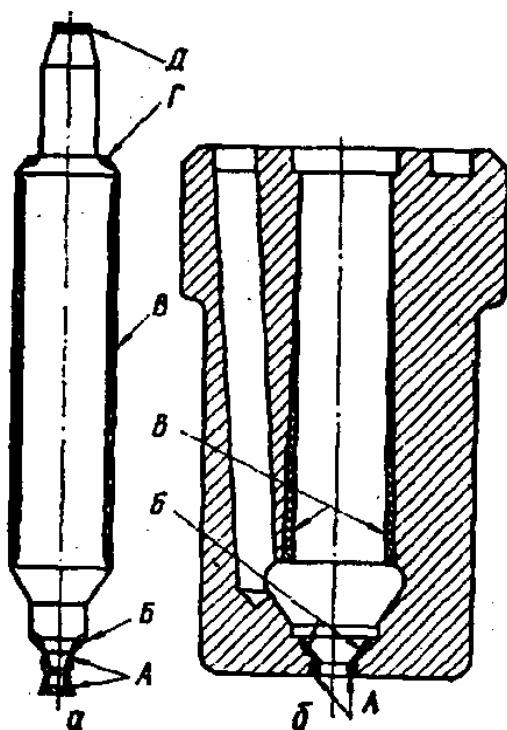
Місця і характер спрацювання деталей розпилювача штифтової форсунки: а – поверхонь голки; А – штифта; Б – запірного конуса; В – напрямної частини; Г – торцевої у спряженні з корпусом форсунки; Д – торцевої у спряженні із стержнем пружини; б – поверхонь корпуса розпилювача: А – сопла; Б – запірного конуса; В – напрямної частини
